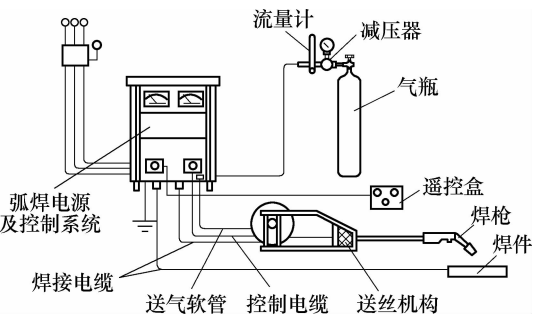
半自动熔化极气体保护焊设备构成
